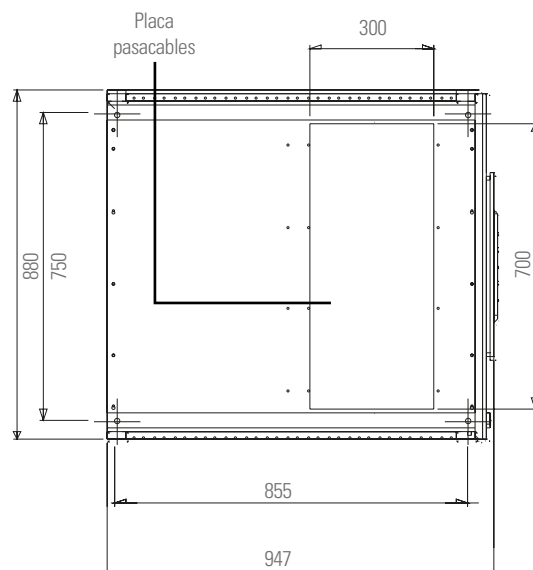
Vista en planta de la base de equipos de 200... 300 kVA.
